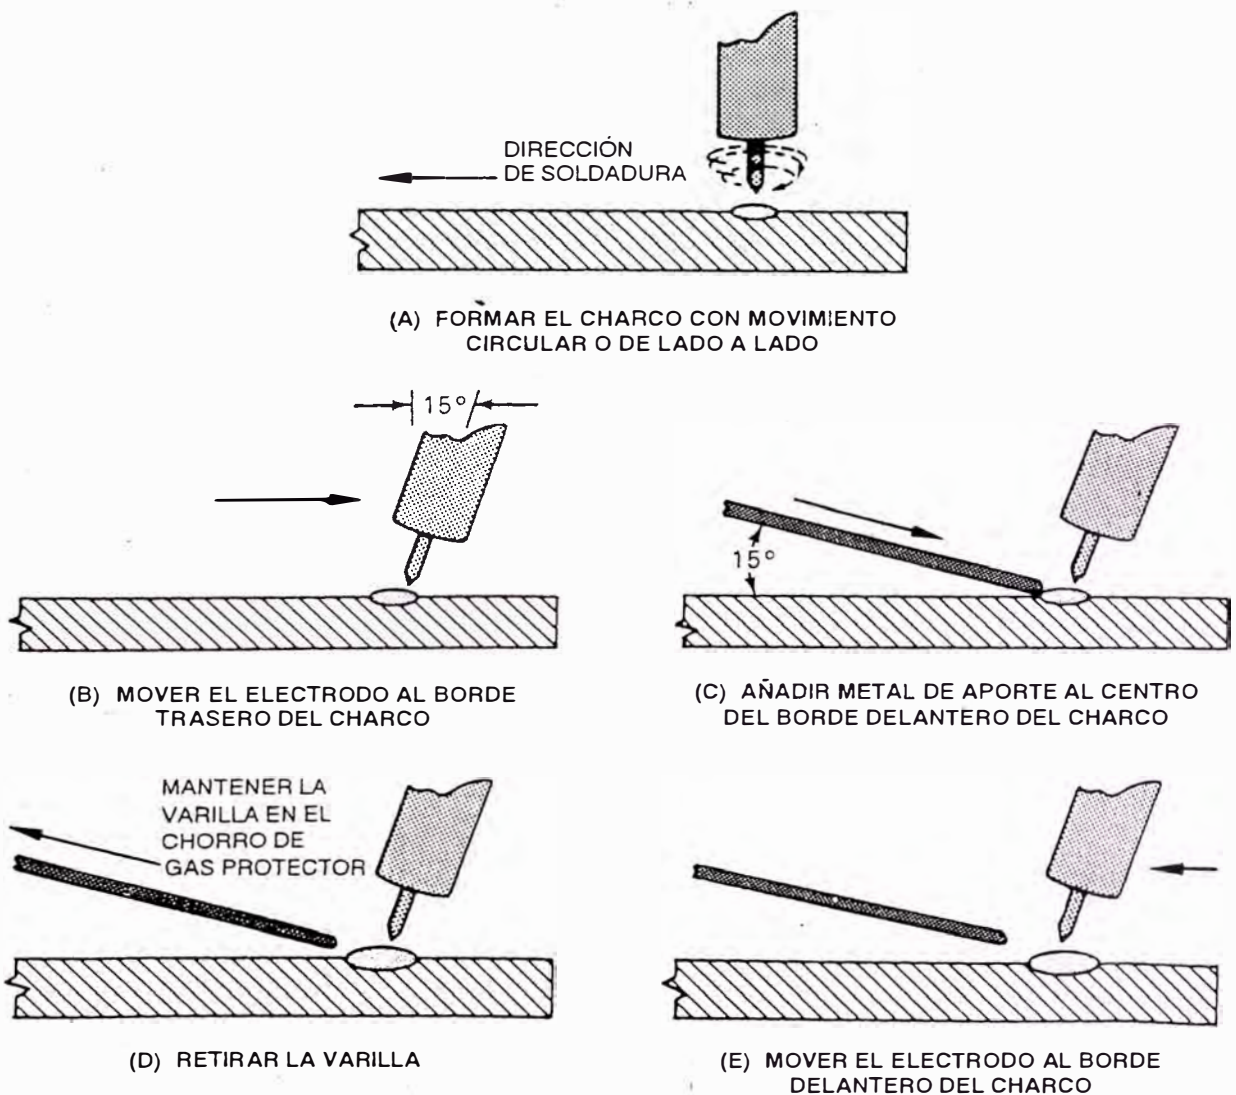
Técnica para soldadura por arco de tungsteno y gas manual
